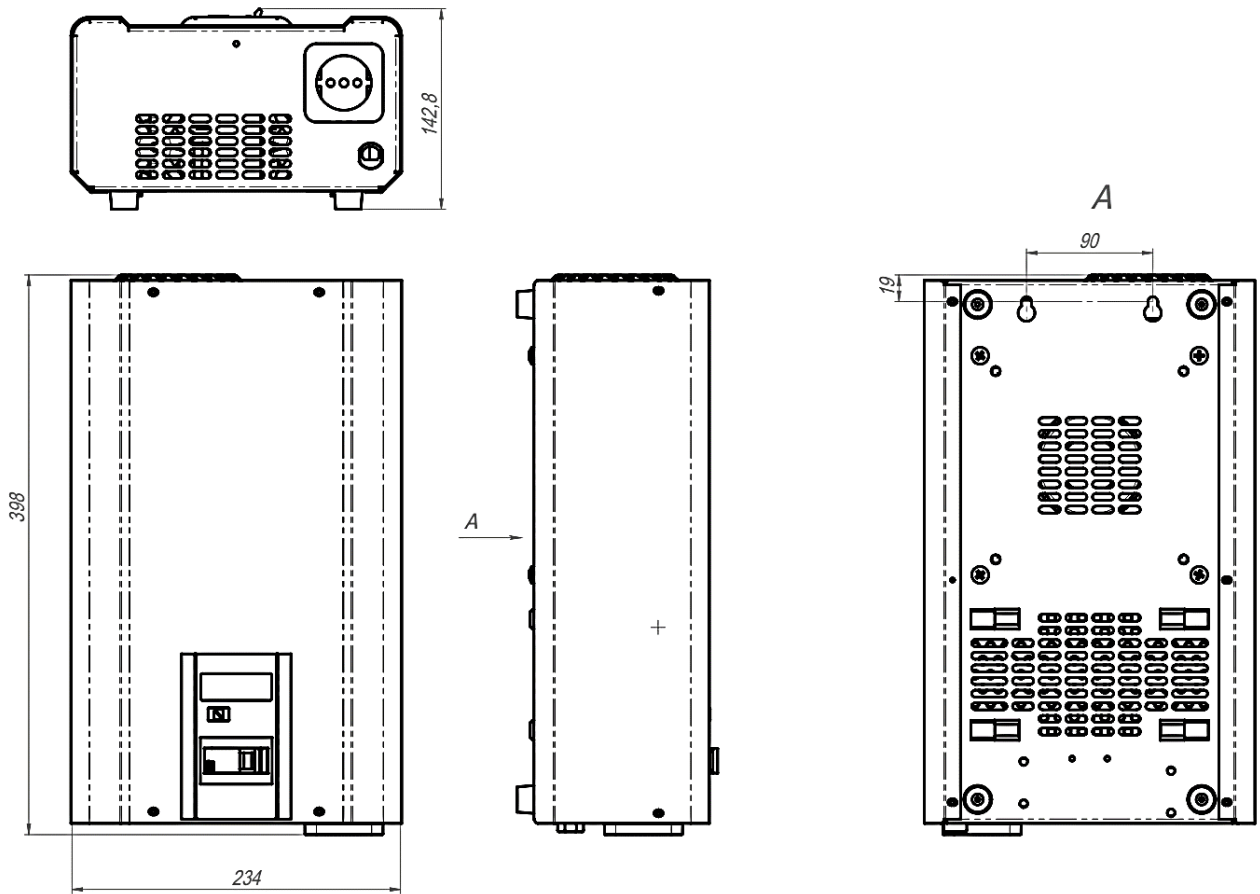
Габаритные и установочные размеры стабилизаторов АМПЕР на 5, 10, 16А
